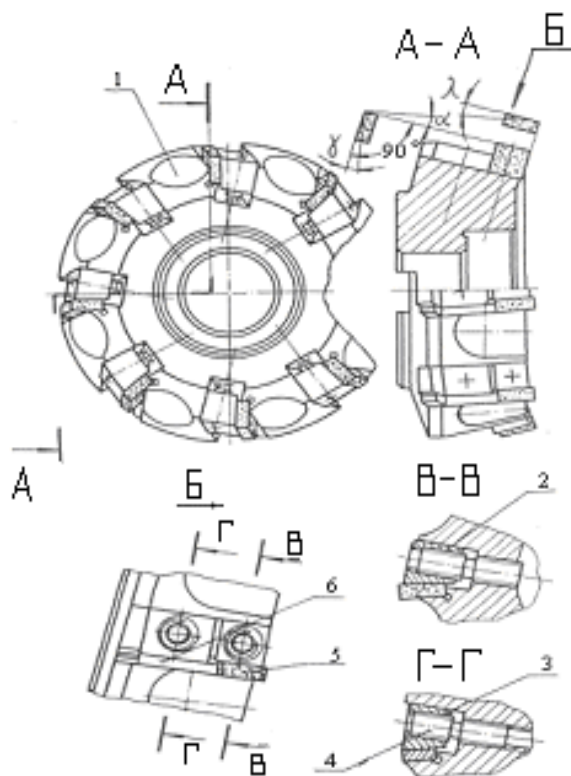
Конструкция фрезы с механическим креплением перетачиваемых восьмилезвийных пластин
